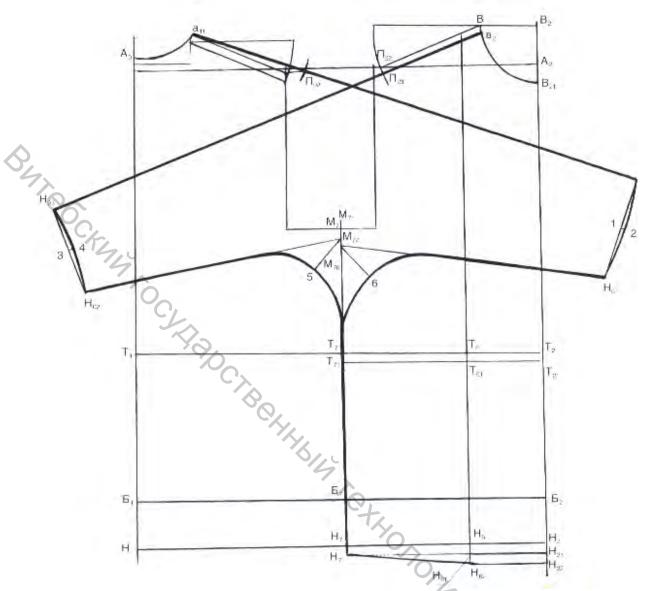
Чертеж стана изделия с цельнокроеными рукавами
